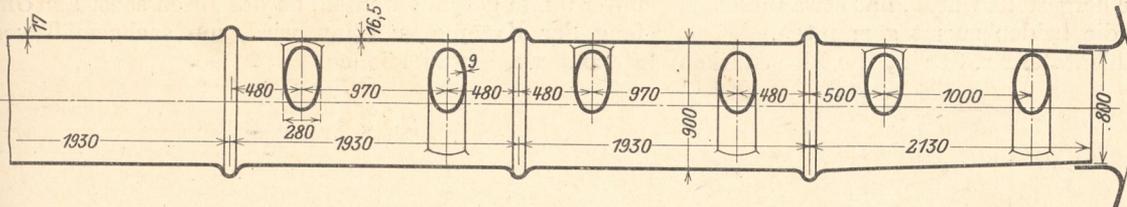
Flammrohr mit Pommé-Wellen und eingeschweißten Quersiedern.
